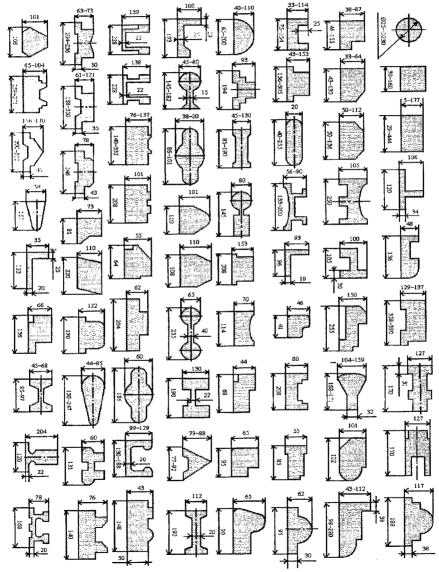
Профили заготовок, получаемых методом ГНД
